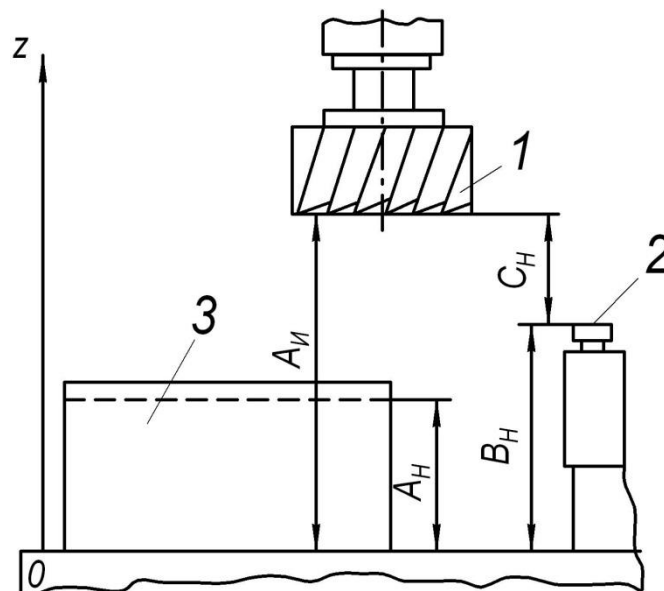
Схема размерной настройки инструментов многоцелевого станка с ЧПУ по оси Z
